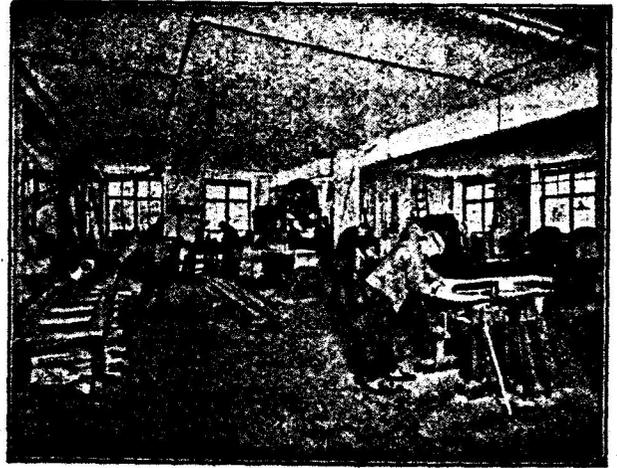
Teilansicht: Maschinensaal für Holzbearbeitung.
